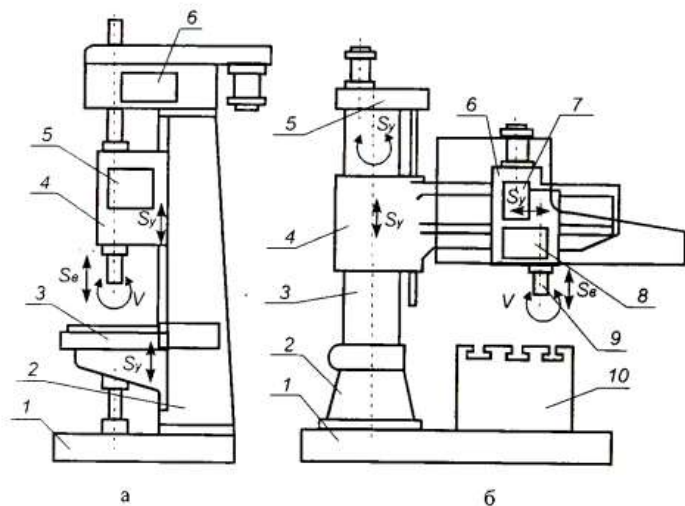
Загальний вигляд вертикально (а) і радіально-свердлильного (б) верстатів
